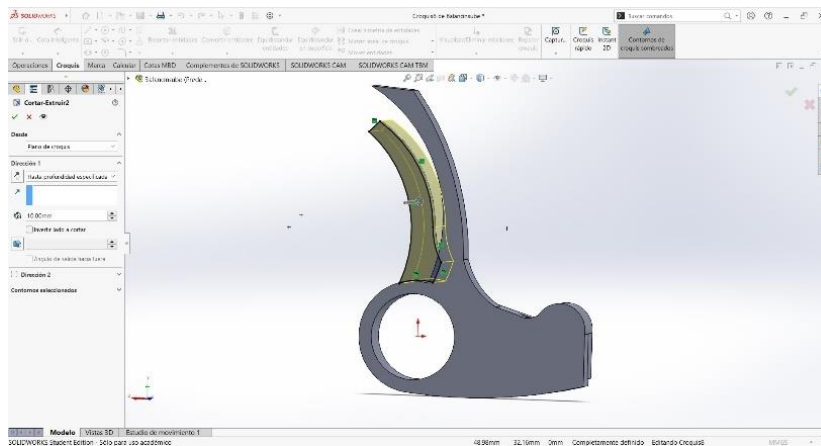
Balancín 1 (Extrusionado de corte de Croquis 4). Fuente: SolidWorks
